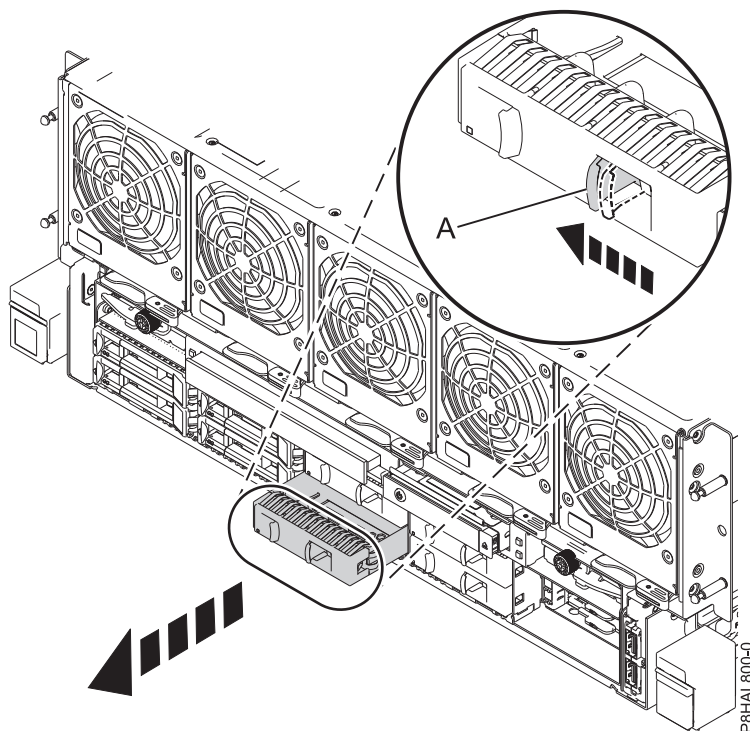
Extracció d'un panell de reblliment d'una unitat de disc d'un sistema 8408-44E o 8408-E8E
